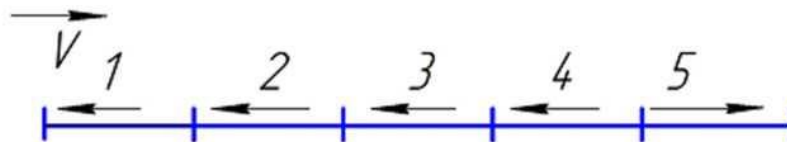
Обратно-ступенчатый способ сварки
